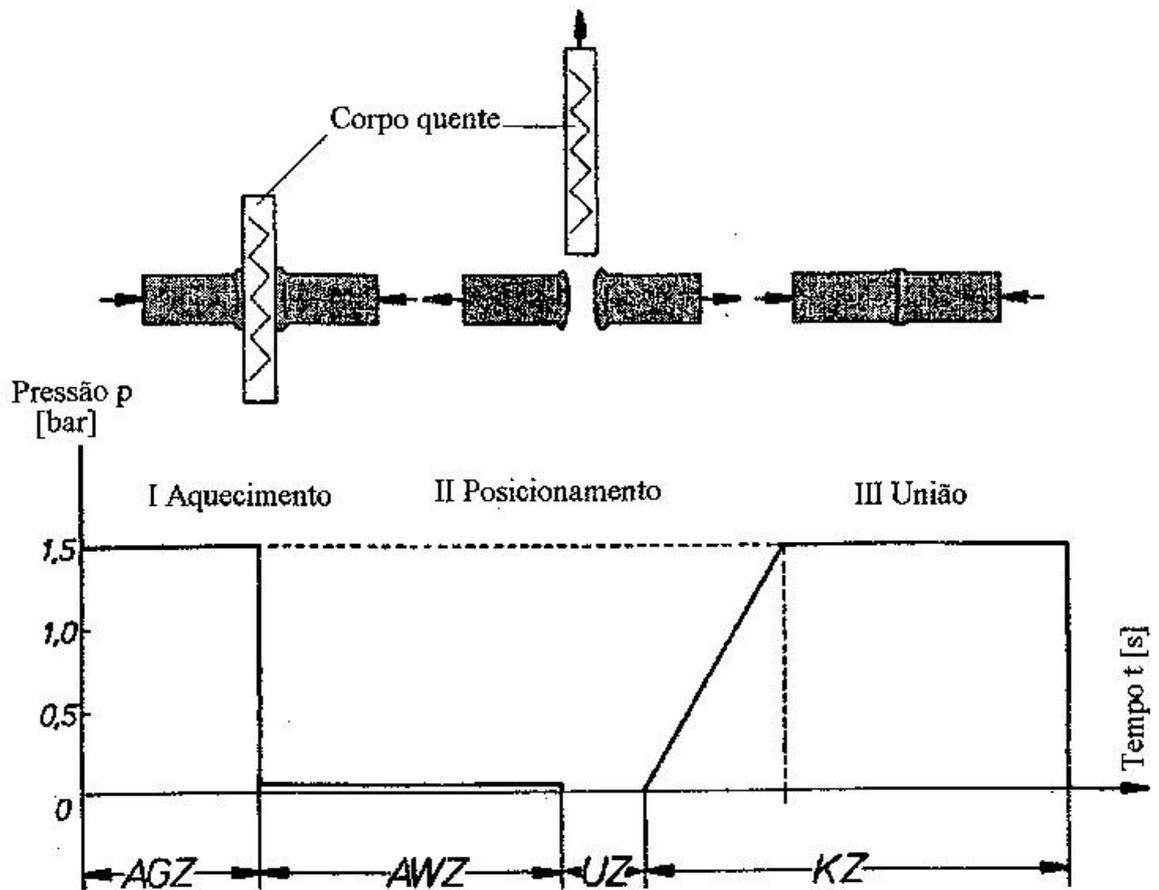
Sequência de soldagem chata por corpo quente (MICHAELI et al.,1995)
